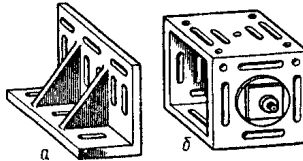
Пристрої для просторового розмічання: а – кутник; б – кубик
